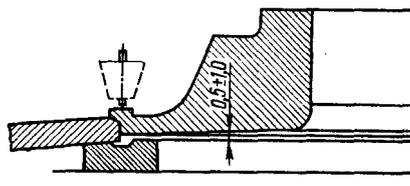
Фланца ресивера *воздушного тормоза грузового автомобиля
